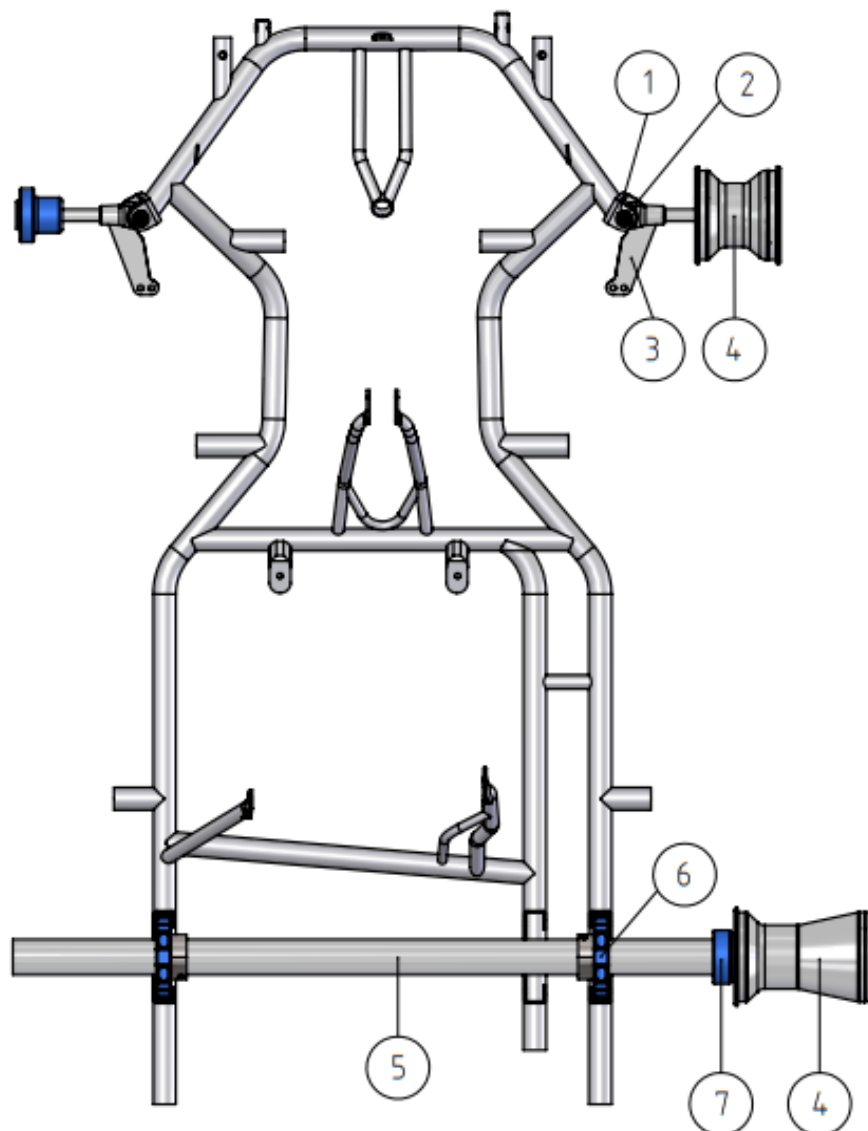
Dibujo técnico N0.1.0A - Bastidor del chasis y partes principales del chasis
